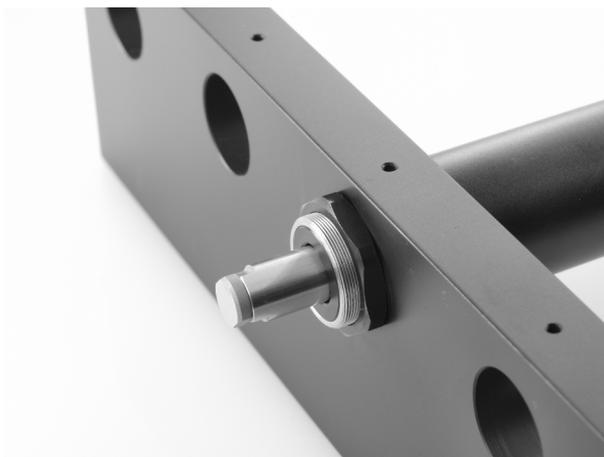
Beispiel für den Einbau eines Linearaktors (hier: M-235)
